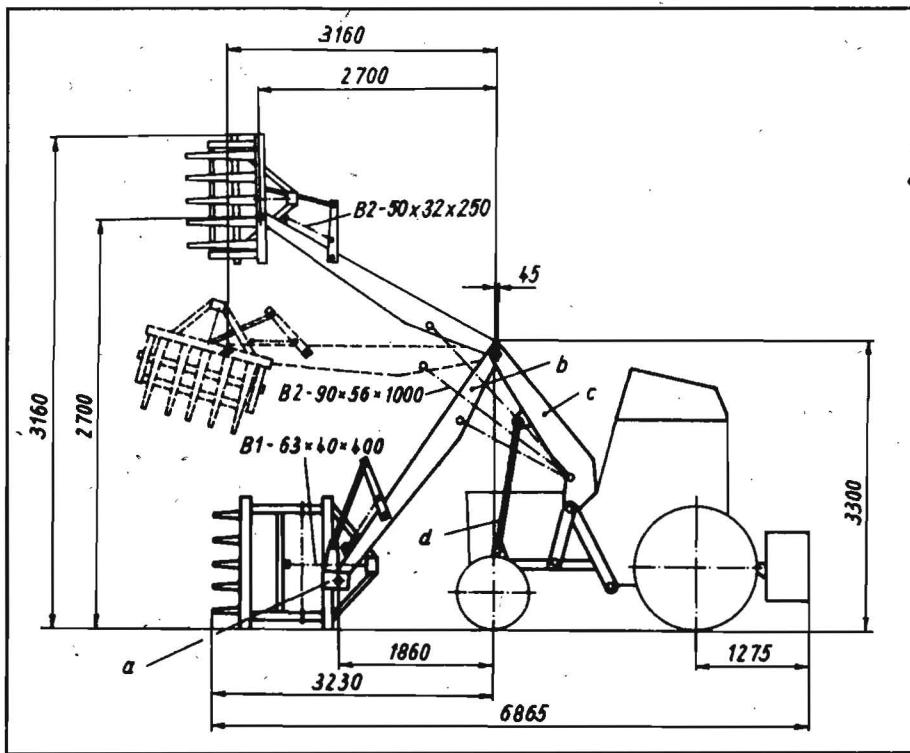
Abmessungen des Frontladers FL 600 mit Zinkengreifer am Traktor MTS-50; a Werkzeughalter, b Knickausleger, c Hubausleger, d Druckstange
